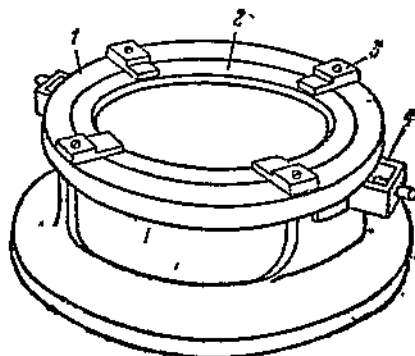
Матрица: 1 — корпус матрицы, 2 — кольцо, 3 — фиксатор, 4 — съемник
